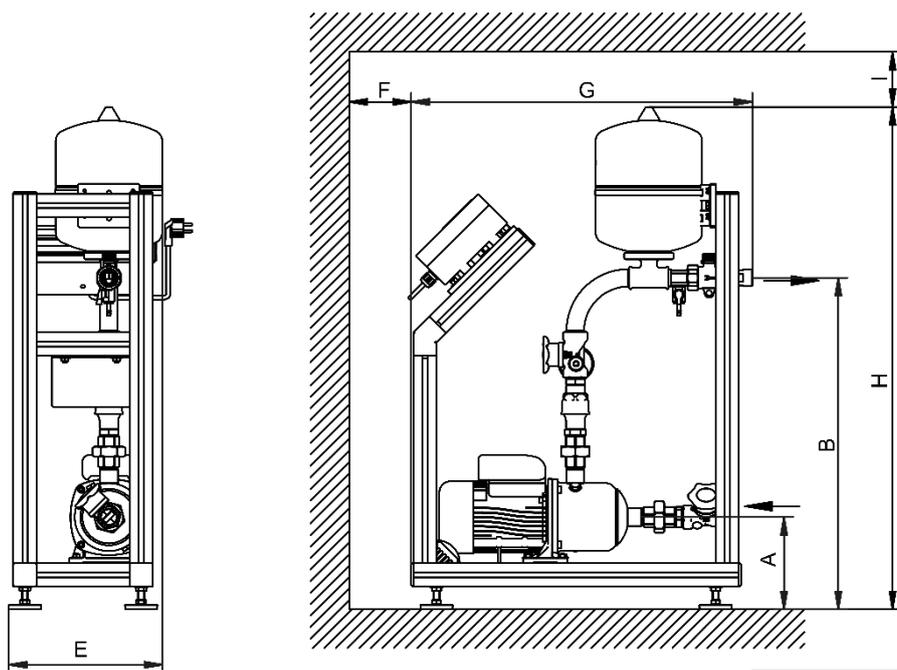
disegno quotato moltiplicatore di pressione singolo GENO-FU-X e GENO-HR-X
